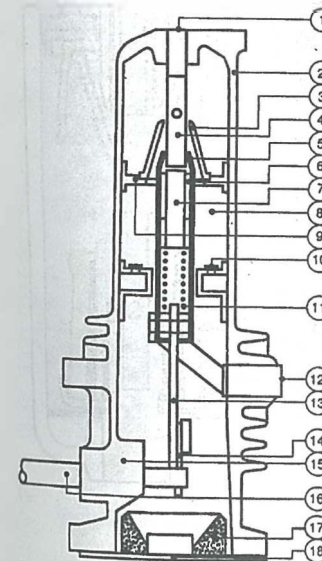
Автокомпрессионный элегазовый выключатель [35]
